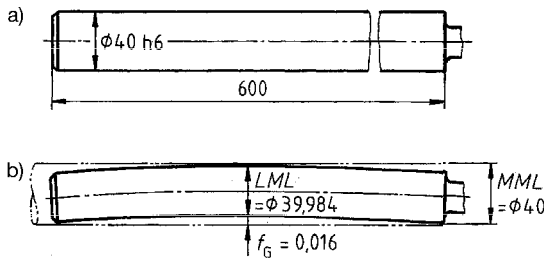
Rundführung aus gehärtetem Stahl. a) Zeichnung, b) zulässige Ausführung
